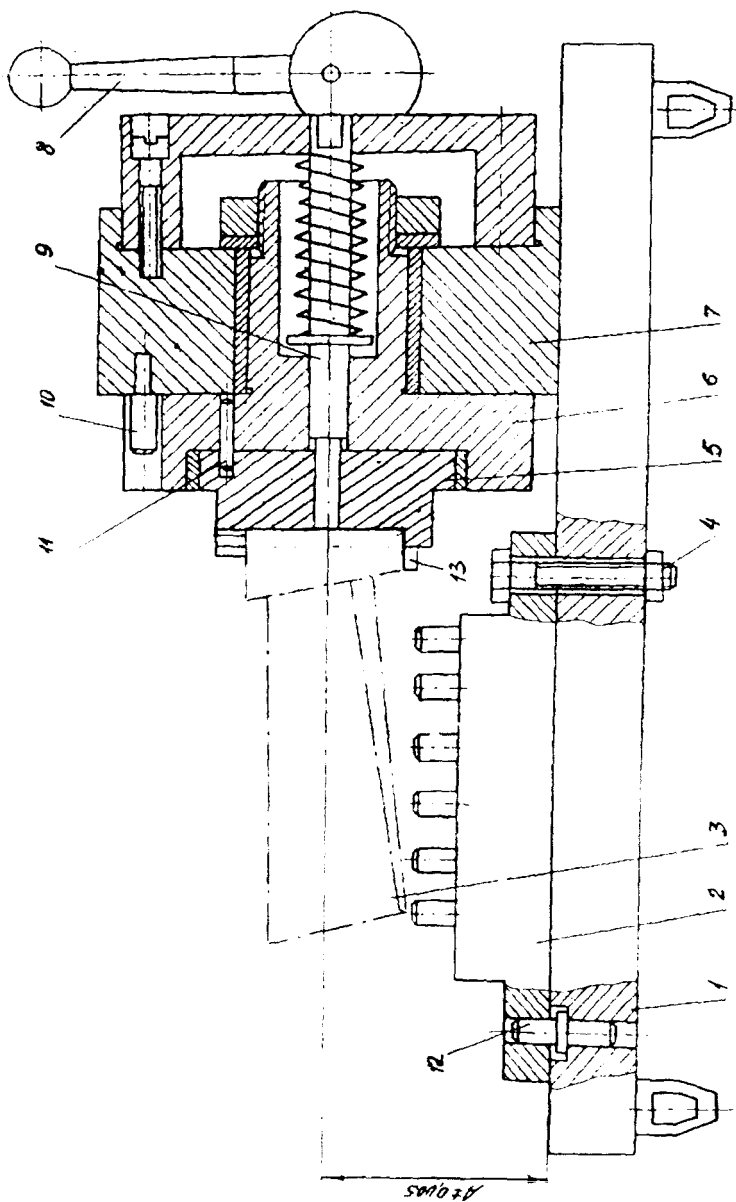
Приспособление для контроля профиля шпильки и корыта рабочих лопаток компрессора
